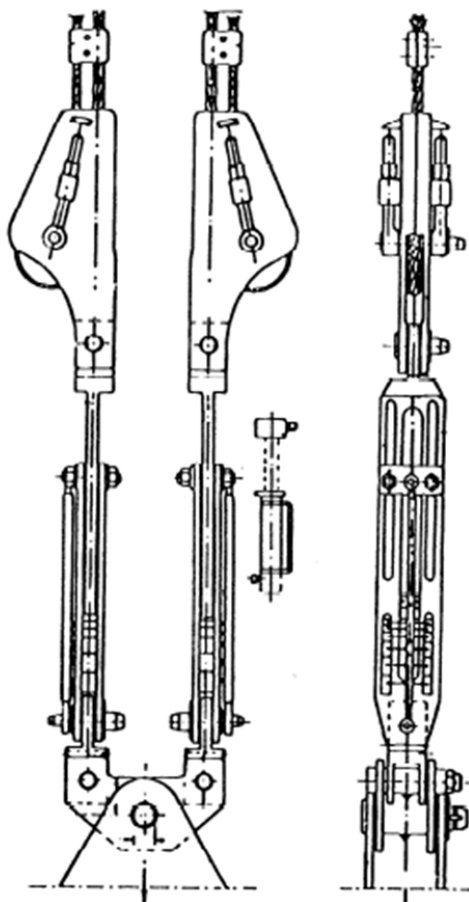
Ejemplo de amarre para instalaciones de polea Koepe multicable con dispositivo de compensación de alargamientos de los cables
